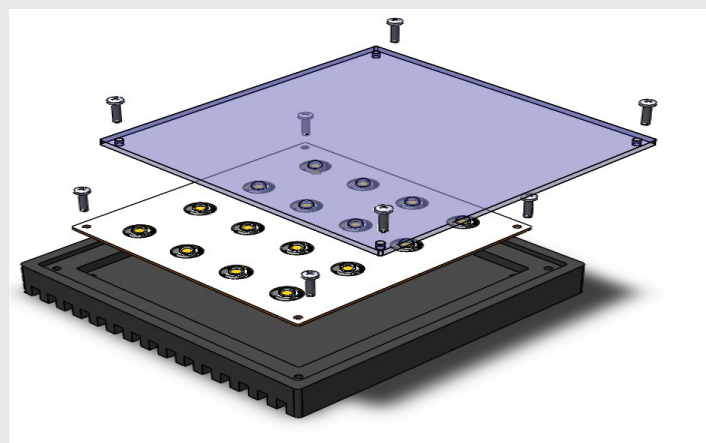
Vista en explosión del ensamble del prototipo de luminaria LED
